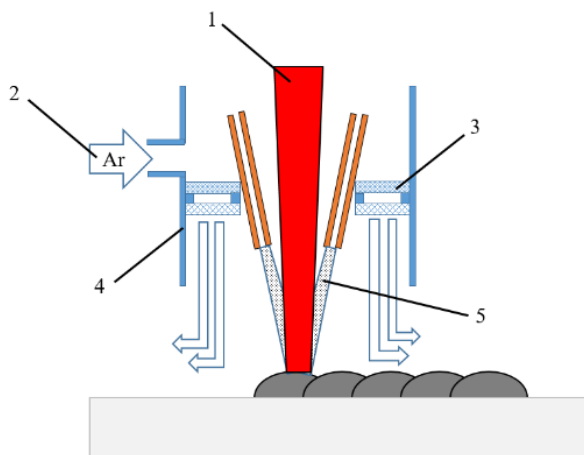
Сопловая насадка: 1 — лазерное излучение; 2 — защитный газ (Ar); 3 — газовая линза; 4 — сопловая насадка; 5 — порошковый материал
